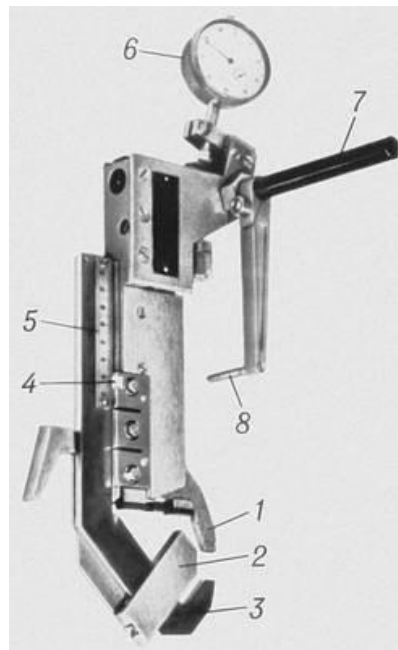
Показывающий прибор активного контроля с навесной скобой: 1, 3 — регулируемые контакты; 2 — контролируемая деталь; 4 — указатель; 5 — шкала для предварительной настройки на размер; 6 — индикатор; 7 — кронштейн; 8 — ограничитель.
